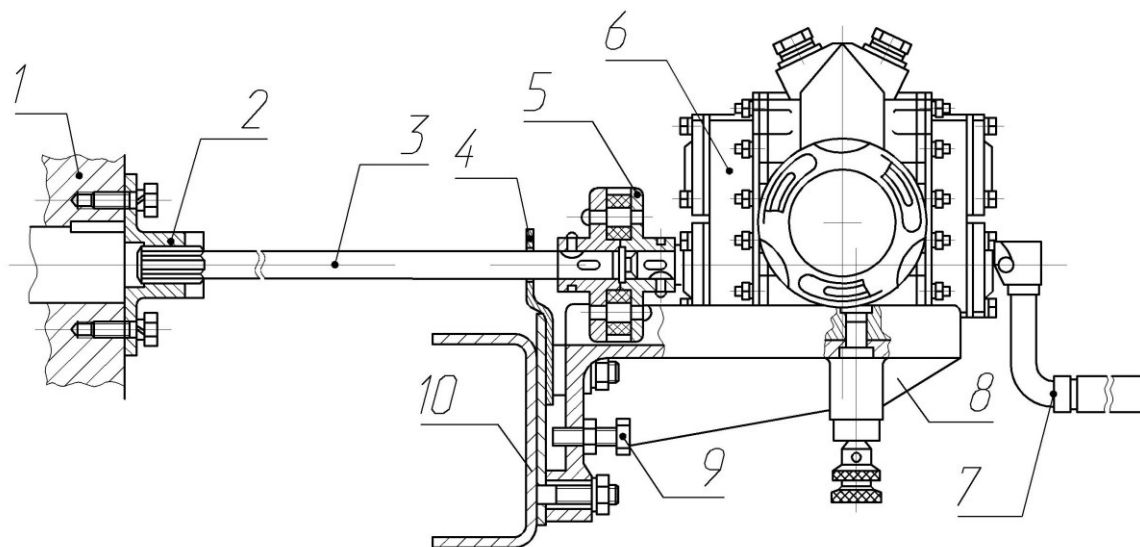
Установка НШН-600 на автомобиле семейства ГАЗ: 1 – шкив коленчатого вала двигателя; 2 – храповик специальный; 3 – вал привода; 4 – кронштейн заводной рукоятки; 5 – муфта соединительная в сборе; 6 – насос; 7 – заводная рукоятка; 8 – кронштейн в сборе; 9 – регулировочный болт; 10 – косынка в сборе.
